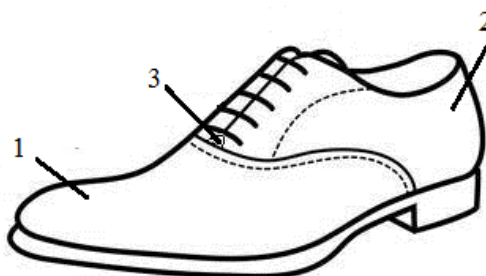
Наружные детали заготовки полуботинка:
